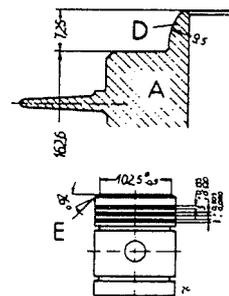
Merkmale von Zylinder und Kolben jetziger Ausführung
